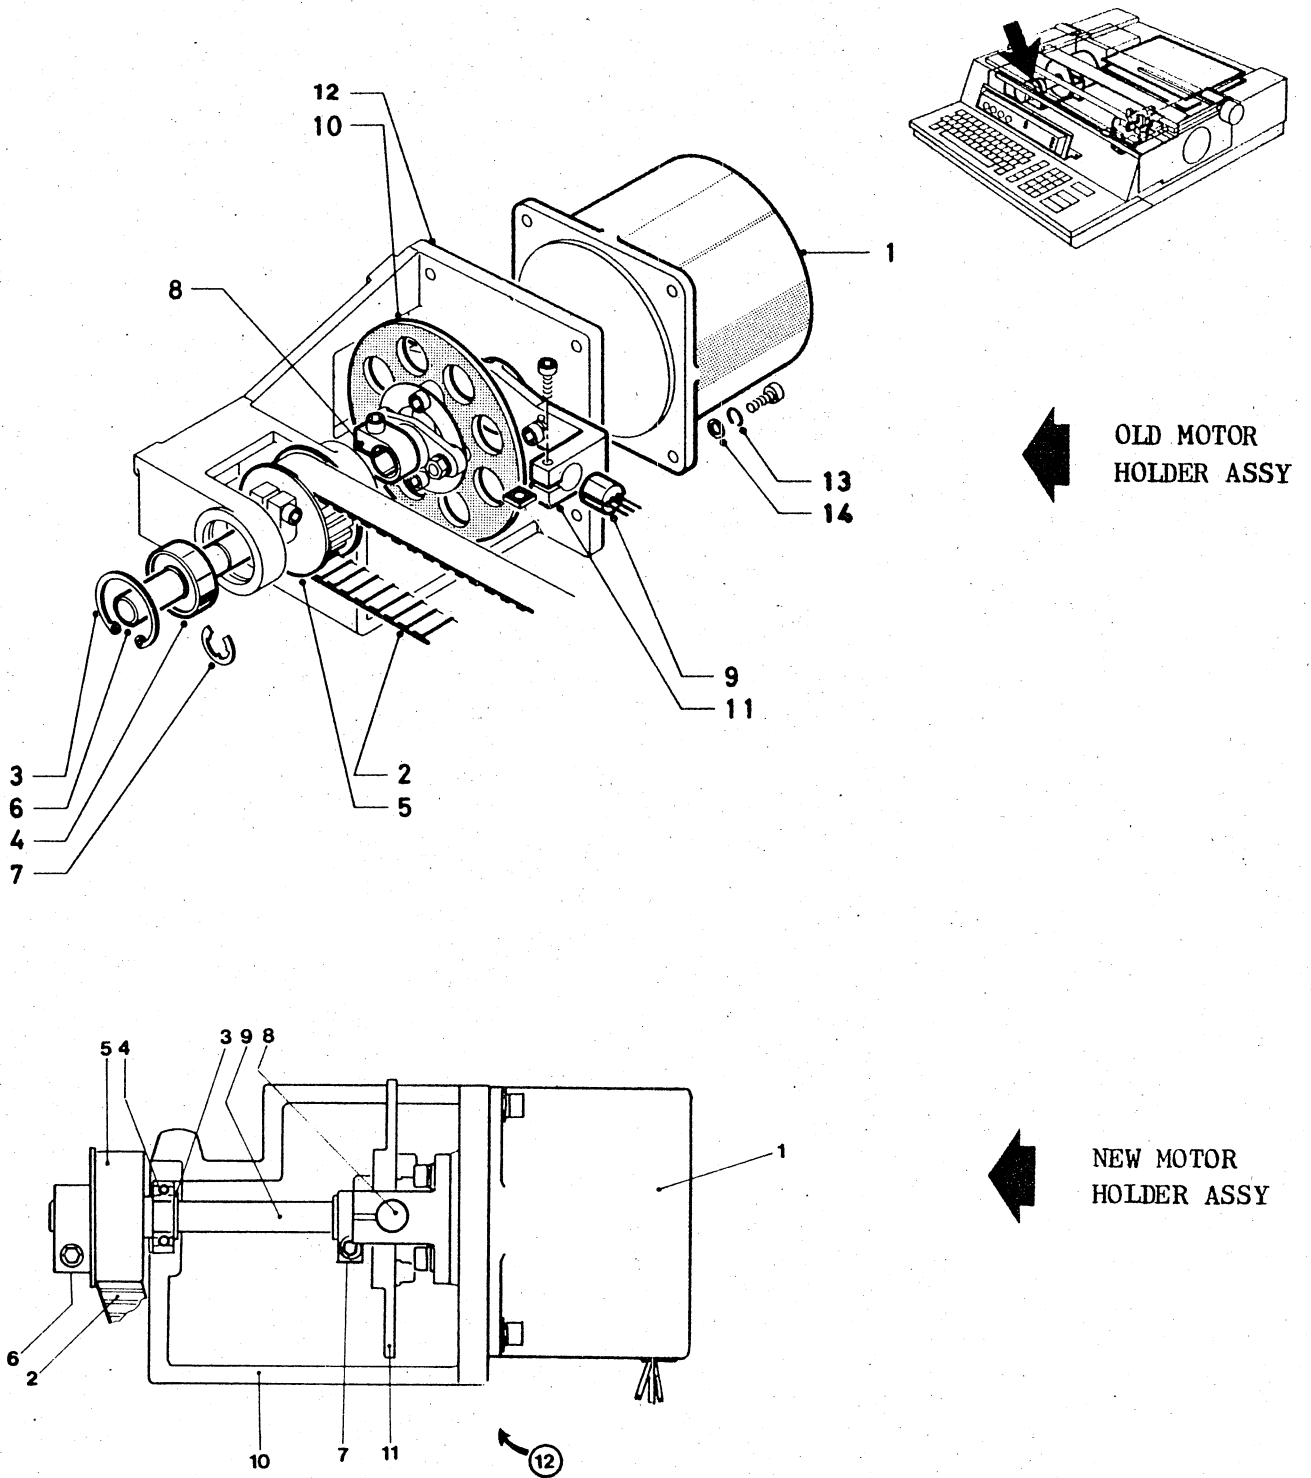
Assieme Supporto Motore - Figure 9-4 Motor Holder Assembly
